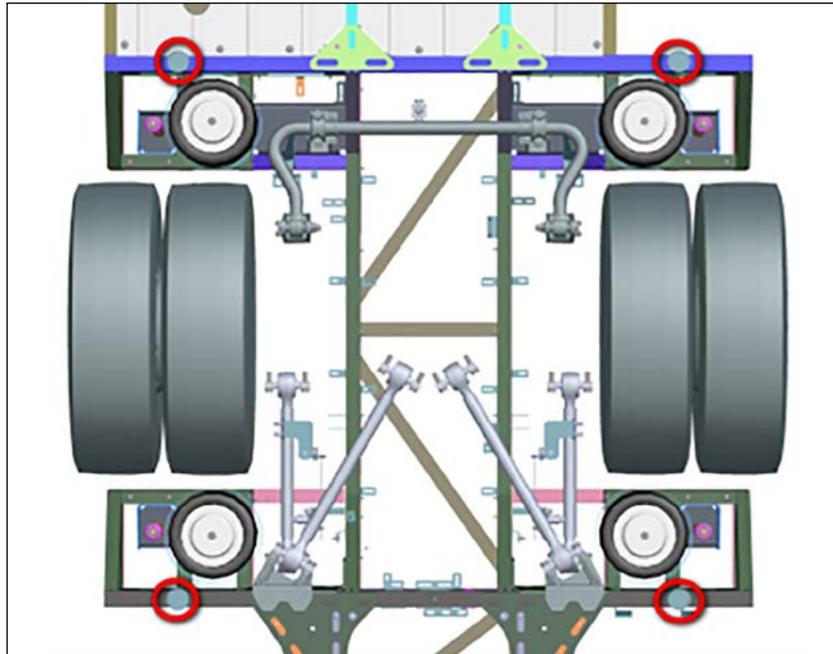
Pontos de apoio para elevação do eixo traseiro
